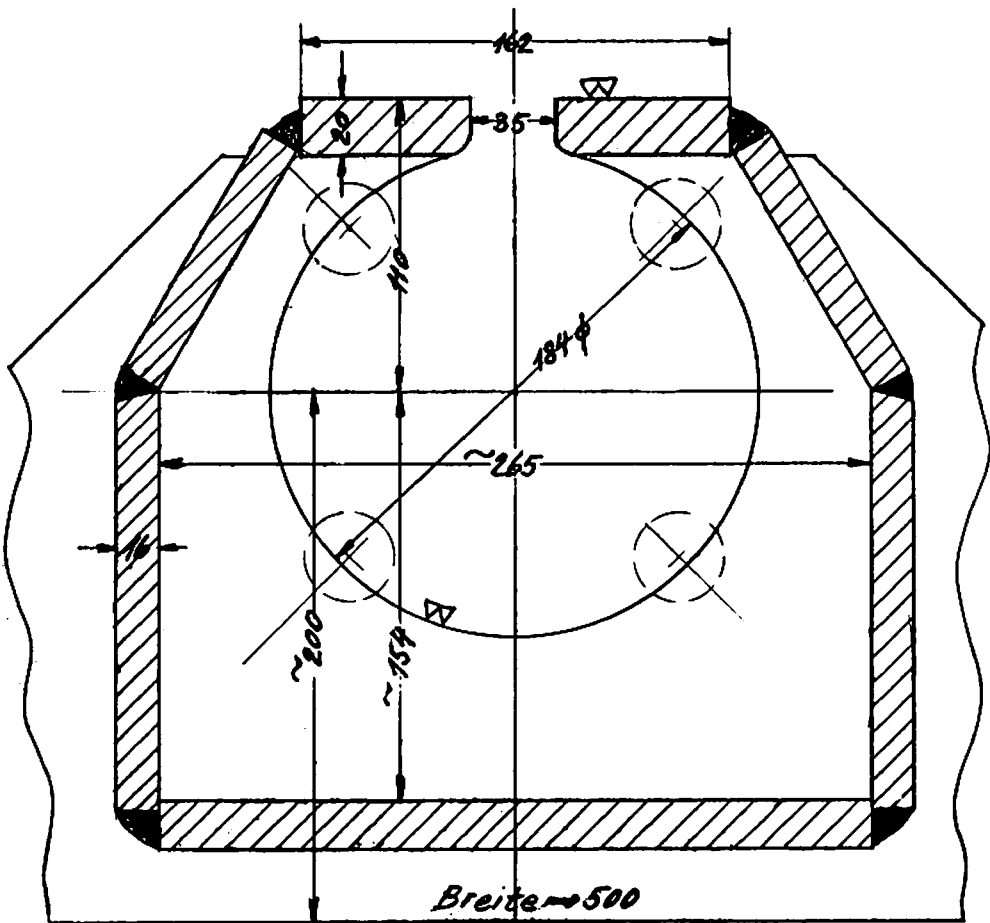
Die einzelnen Blechteile des Gehäuses.
